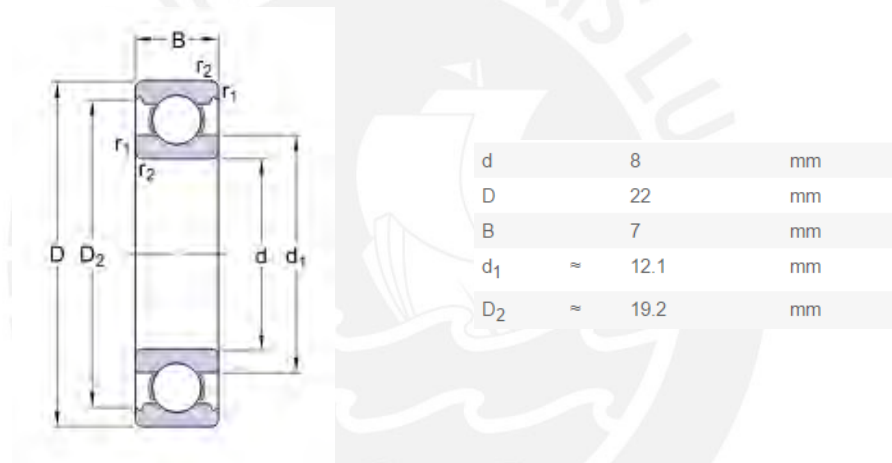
Dimensiones del rodamiento SKF 608<sup>12</sup>
